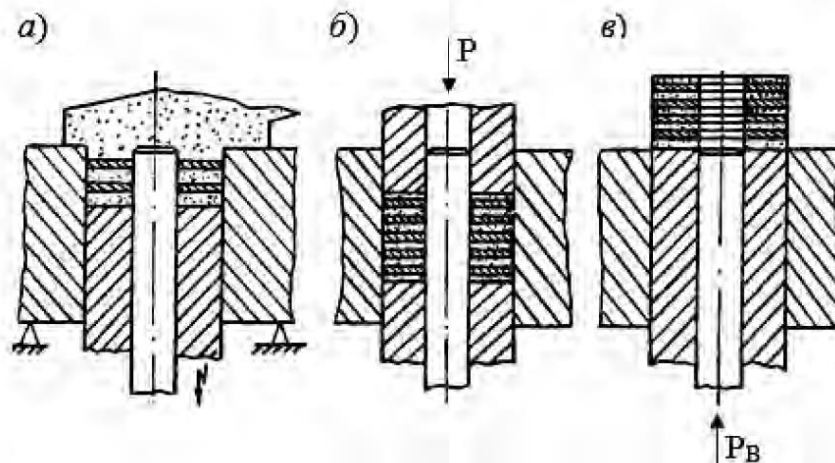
Схема пакетного прессования шайб: а – загрузка порошка и установка прокладок; б – одно- или двустороннее прессование; в – выпрессовка пакета
